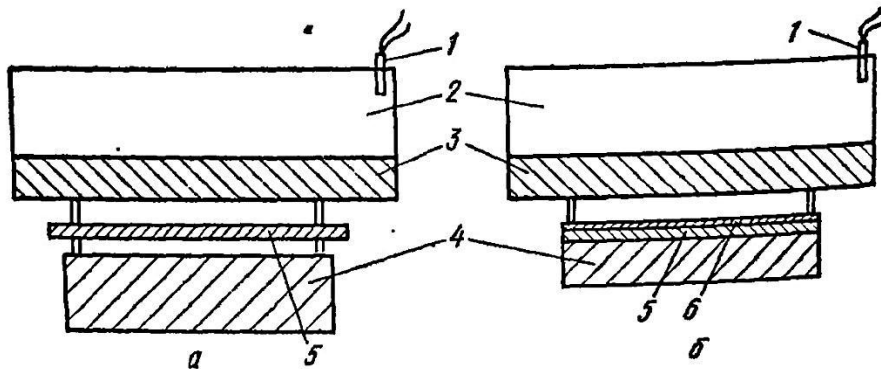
Схемы одновременной сварки пластин.
